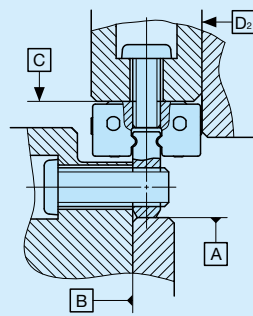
Superfície de montagem de referência de LWL1...Y e estrutura de montagem típica ①
